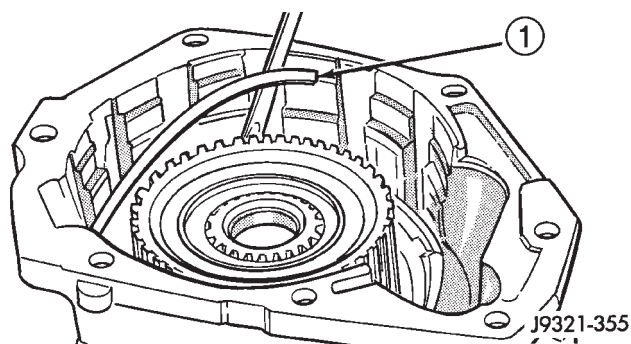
Desmontaje e instalación del muelle ondulado del embrague de sobremarcha
